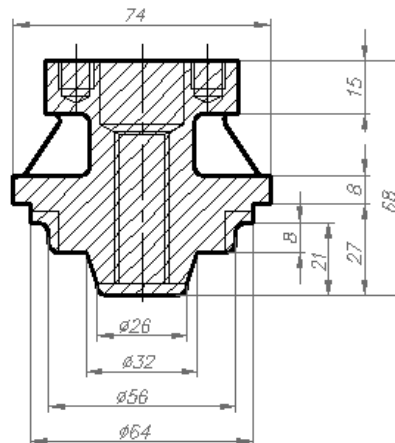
Ескіз заготовки для литва в земляні форми
